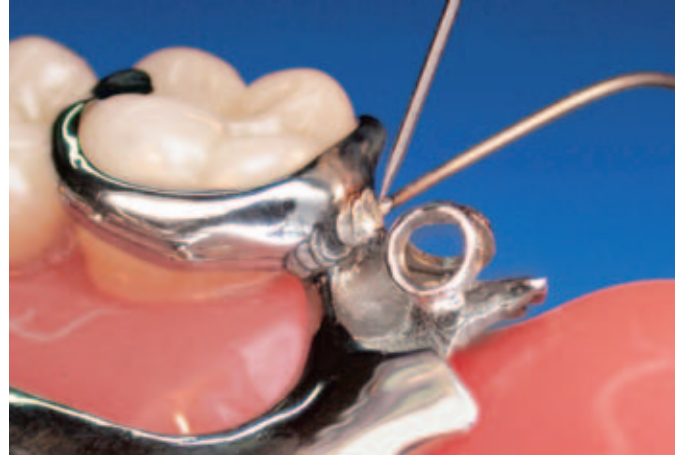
Die Zugabe von artgleichem Material ist immer möglich und erfolgt unter direkter Sichtkontrolle des Zahntechnikers.
